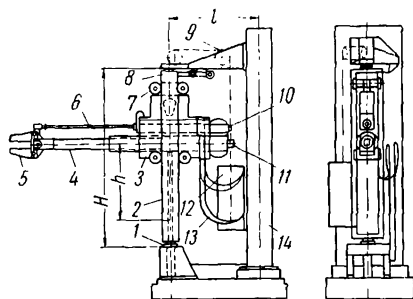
Общий вид консольного поворотного манипулятора для подачи инструмента: 1 — подшипник; 2 — направляющая рама; 3 — каретка; 4 — хобот; 5 — клещевой зажим; 6 — тяга; 7 — колеса каретки; 8 — подшипник; 9 — система блоков; 10 и 11 — пневматические цилиндры; 12 — противовес; 13 — гибкий шланг; 14 — опорная металлическая стойка
